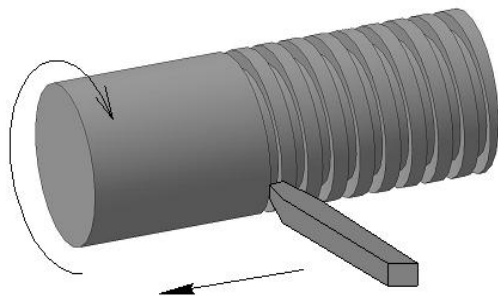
Схема нарезания резьбы на цилиндрическом стержне резцом
